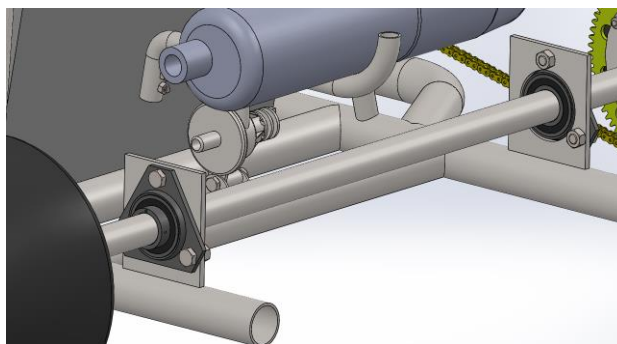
Rodamientos unidos mediante tornillos y soportes soldados al chasis.
